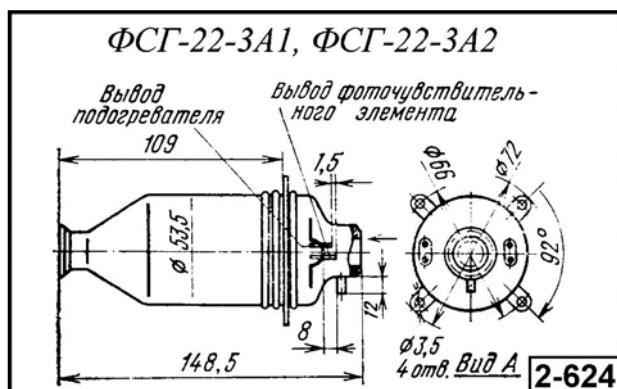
Внешний вид и габаритные размеры охлаждаемых фоторезисторов ФСГ-22-3А1, ФСГ-22-3А2
